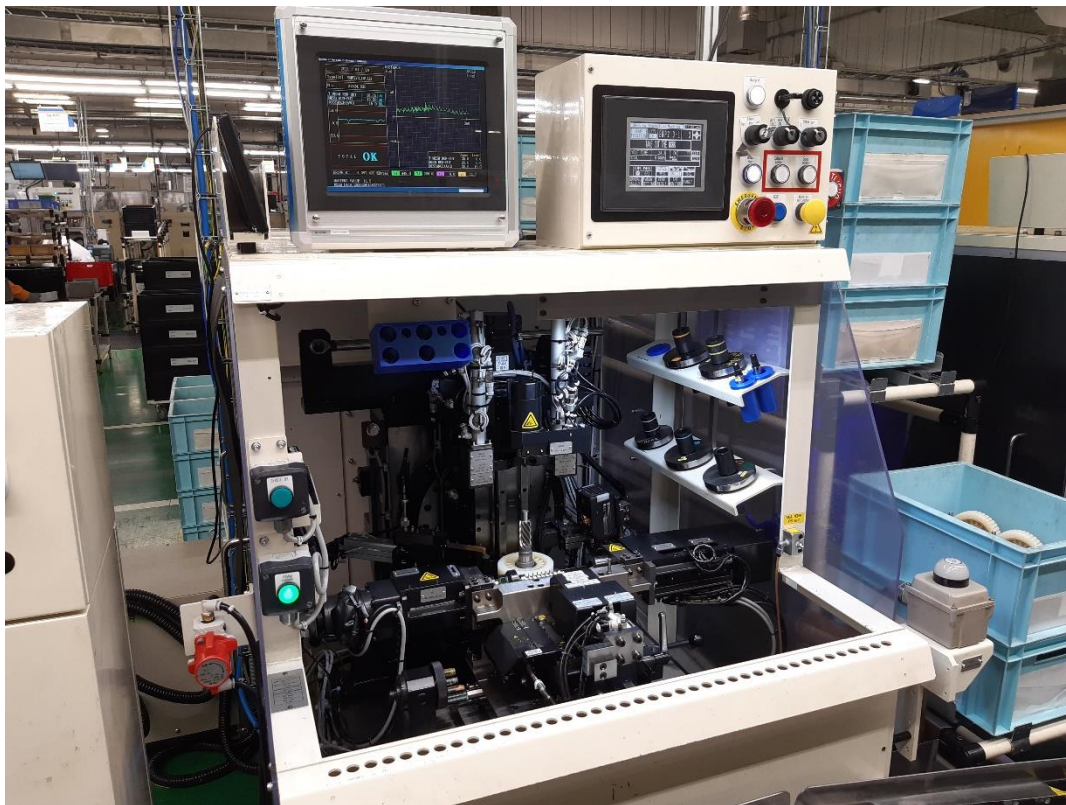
Stroj PWS230 Thread grinding [4]
